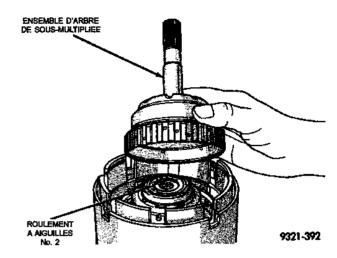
Pose d'ensemble d'arbre de sousmultipliée
